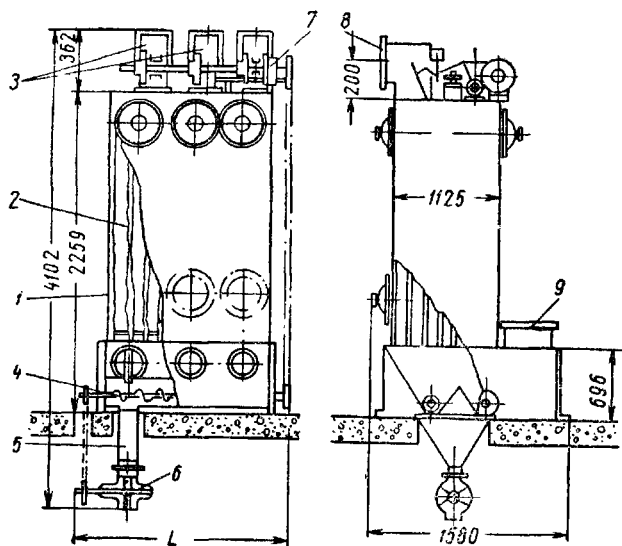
Фильтр рукавный тканевый закрытый всасывающего типа марки ФВ (ФВ-30; ФВ-45; ФВ-60; ФВ-90)
